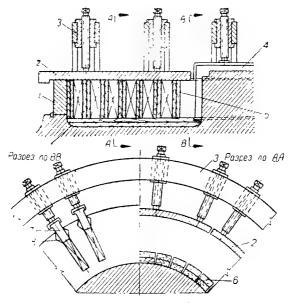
Прессующие приспособления для опрессовки роторных обмоток:
